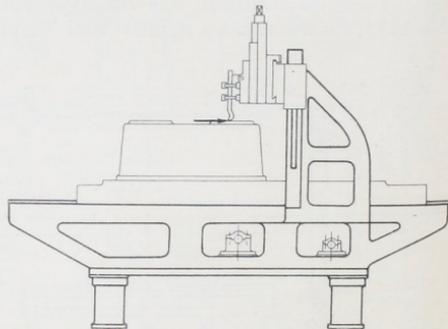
Hobelmaschinenrahmen älterer Form.
